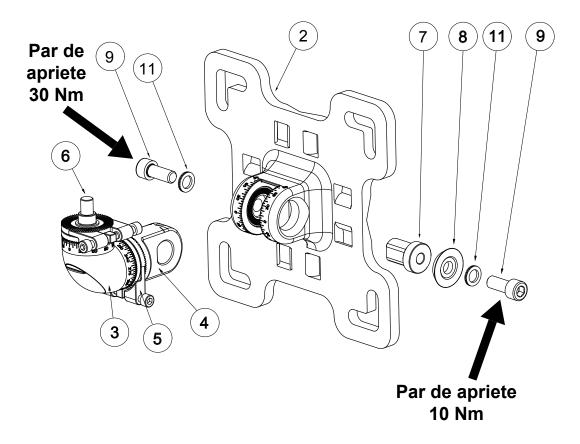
Cambio del adaptador de la placa de montaje para el soporte de montaje universal
